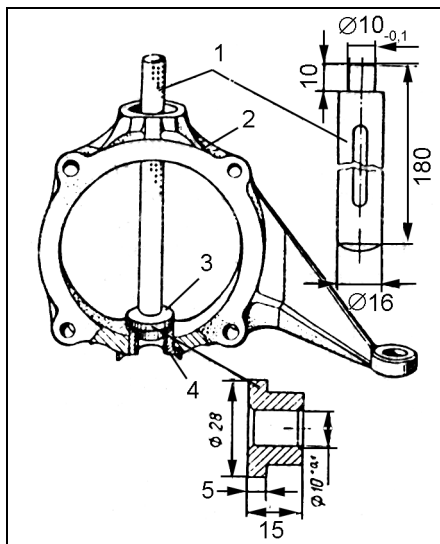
Выпрессовка корпусов втулок шкворней с втулками в сборе: 1 — ручка; 2 — кулак поворотный; 3 — оправка; 4 — корпус втулки шкворня с втулкой в сборе.
